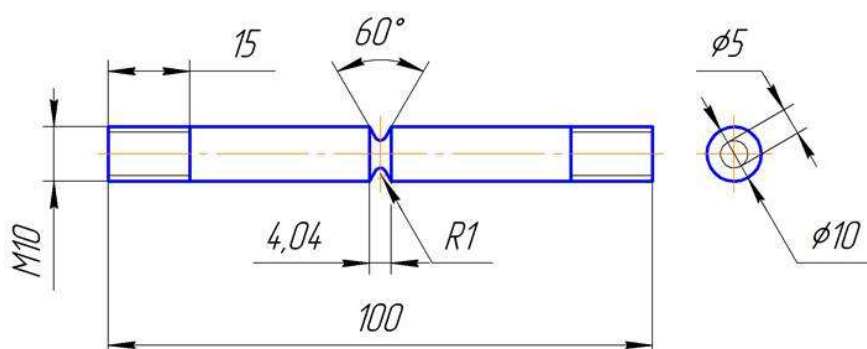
Чертёж образца для испытаний на статическое растяжение.
